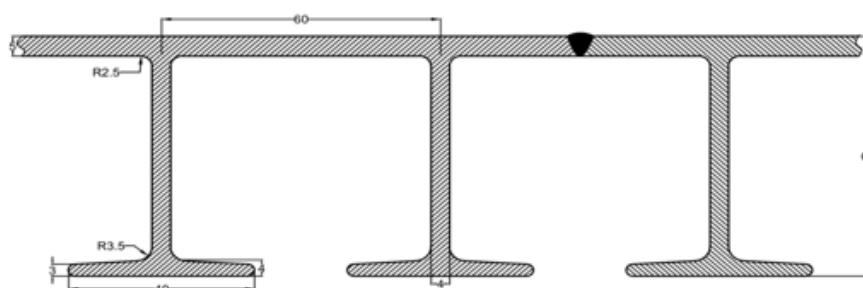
Сварной настил из алюминиевого сплава АМг6
